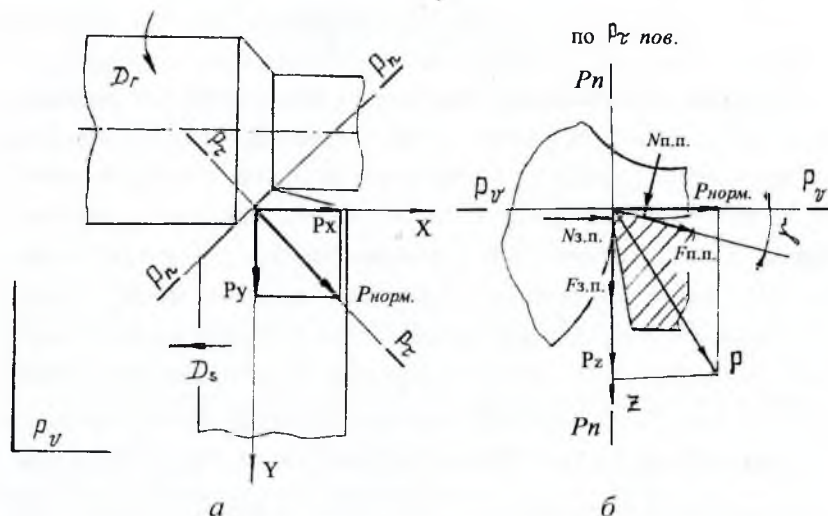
Схема сил, действующих на резец: а – проекция резца и обрабатываемой заготовки на основную плоскость  $P_v$  (вид в плане);
